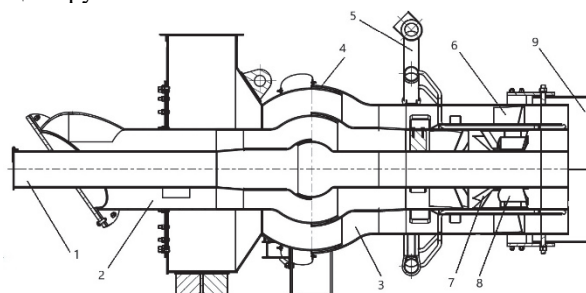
Боковой вид горелки в разрезе: 1 – центральный канал (место размещения запального устройства и мазутной форсунки); 2 – канал подачи аэросмеси; 3 – канал подачи вторичного воздуха; 4 – узел сопряжения статичной и поворотной частей горелки; 5 – газовый коллектор; 6 – аксиальный лопаточный аппарат канала вторичного воздуха; 7 – аксиальный лопаточный аппарат канала аэросмеси; 8 – рассекатели потока аэросмеси; 9 – выходная насадка для горизонтального поворота.
